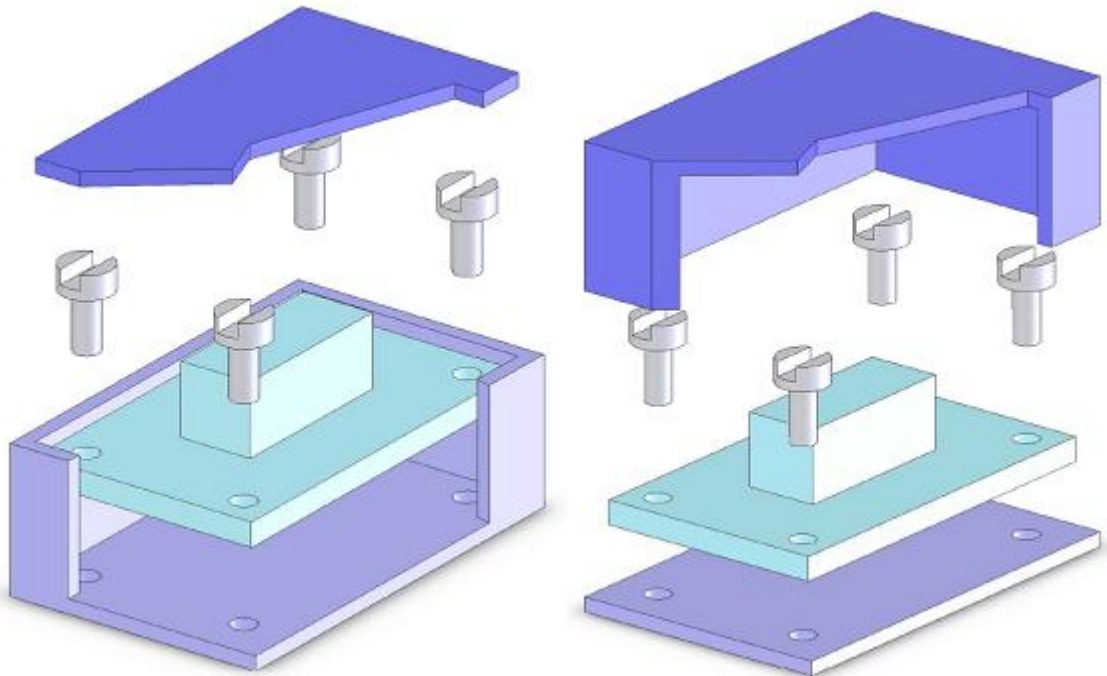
Exemplo de conjunto com a facilitação de acesso durante a montagem
